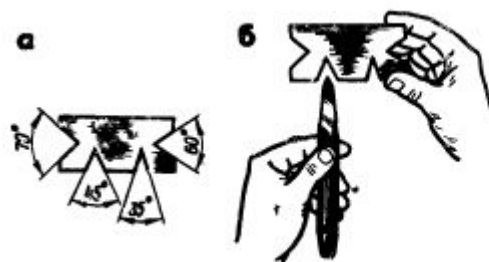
Шаблон (а) и проверка им угла заточки зубила (б)
